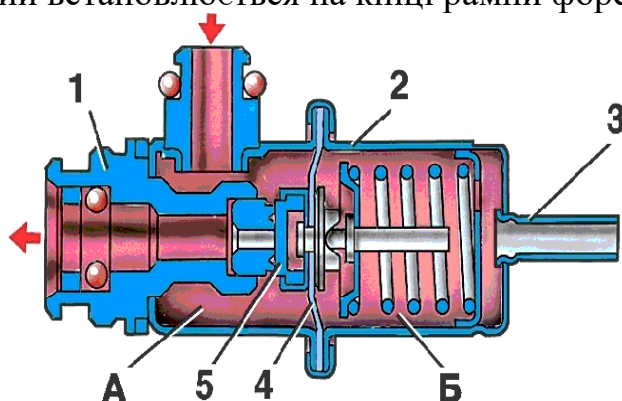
Регулятор тиску палива: 1 - корпус; 2-кришка; 3-патрубок для вакуумного шланга; 4 - діафрагма; 5 - клапан; А - паливна порожнина; Б - вакуумна порожнина.
